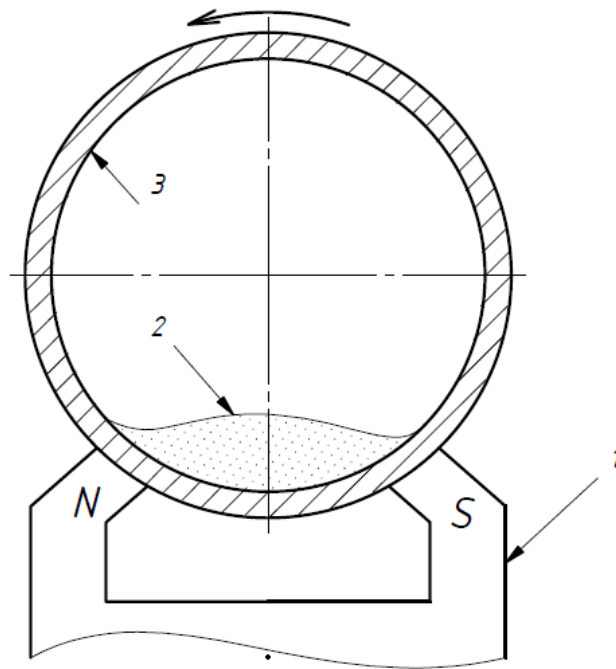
Схема МАО внутрішніх поверхонь циліндричних деталей
